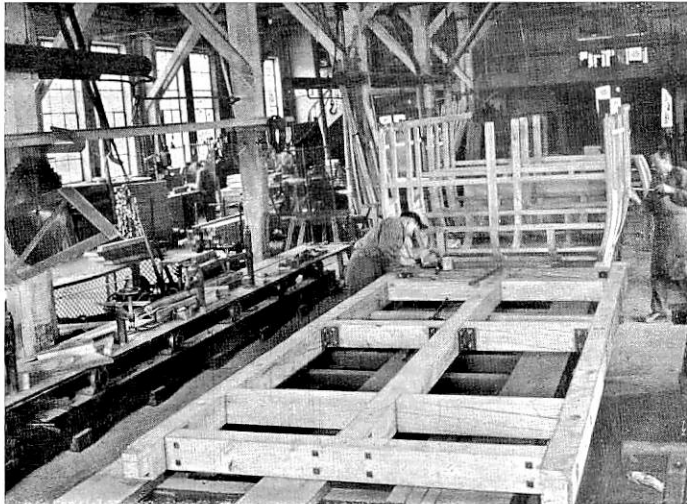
Bau eines Untergestelles und Gerippeaufbau.
